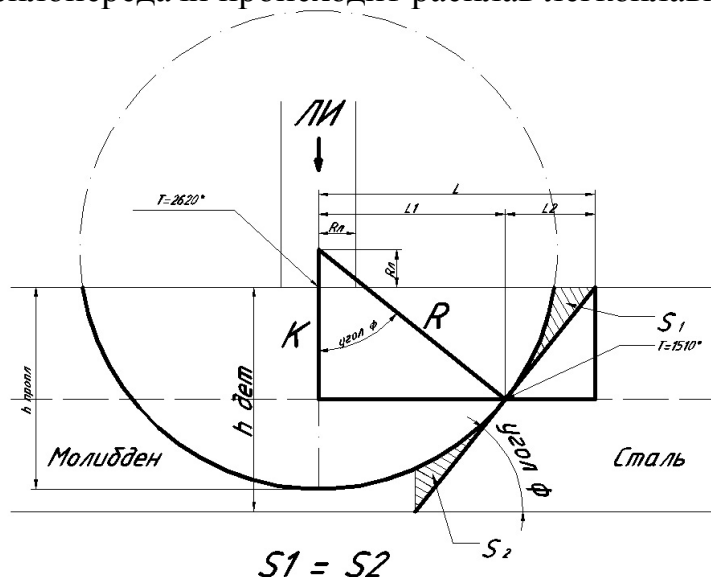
Геометрия стыкового соединения при сварке молибдена и стали
